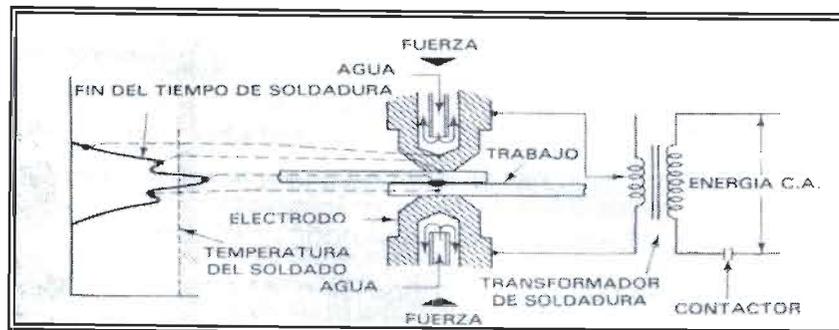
Diagrama proceso de soldadura RSW
